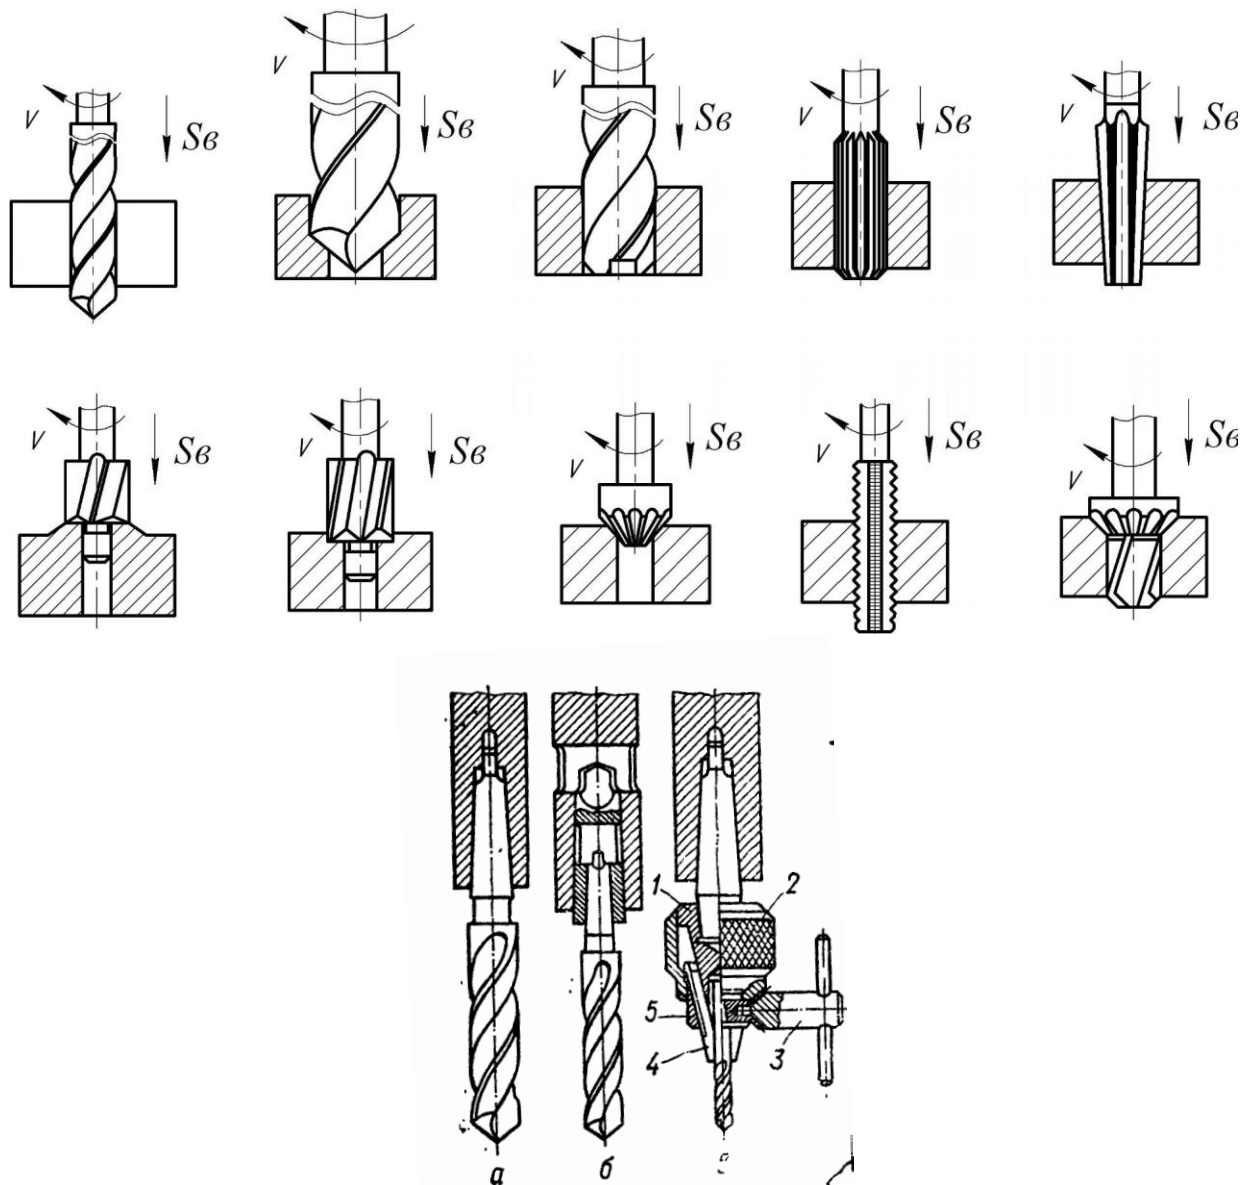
Схеми обробки заготовок та кріплення на свердильних верстатах
